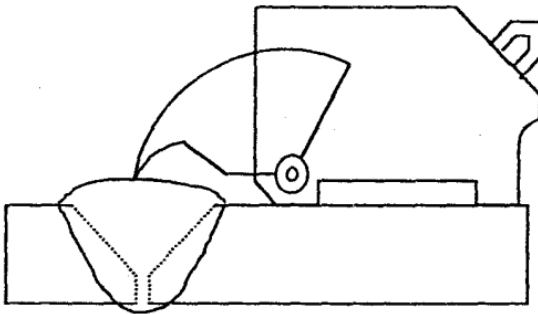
Determinación del refuerzo de la Soldadura
